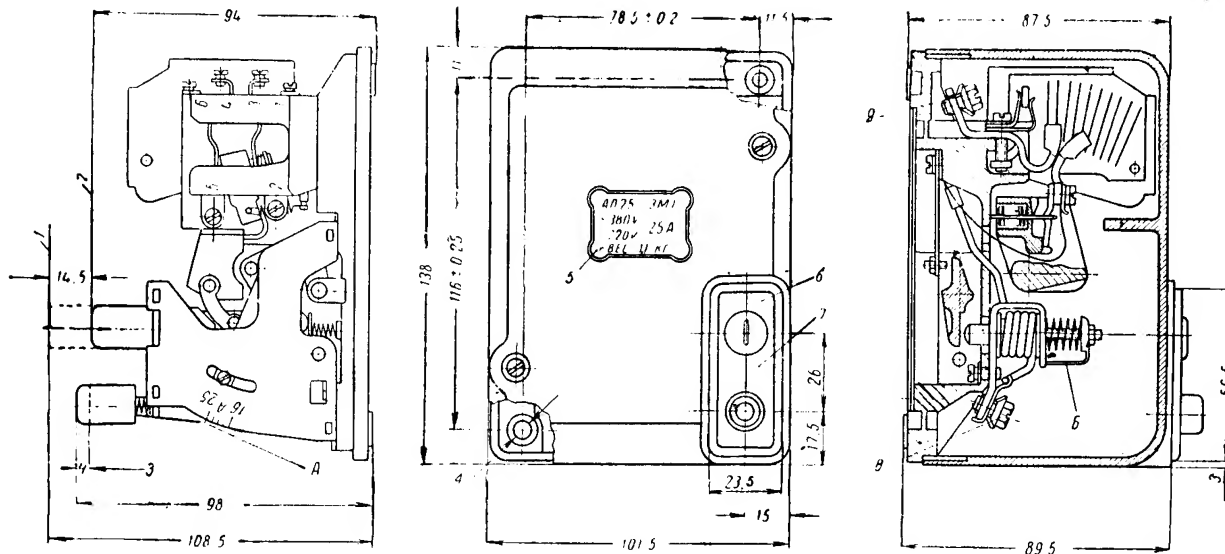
Габаритные и установочные размеры автоматического выключателя типа АП125 в пластмассовом корпусе
